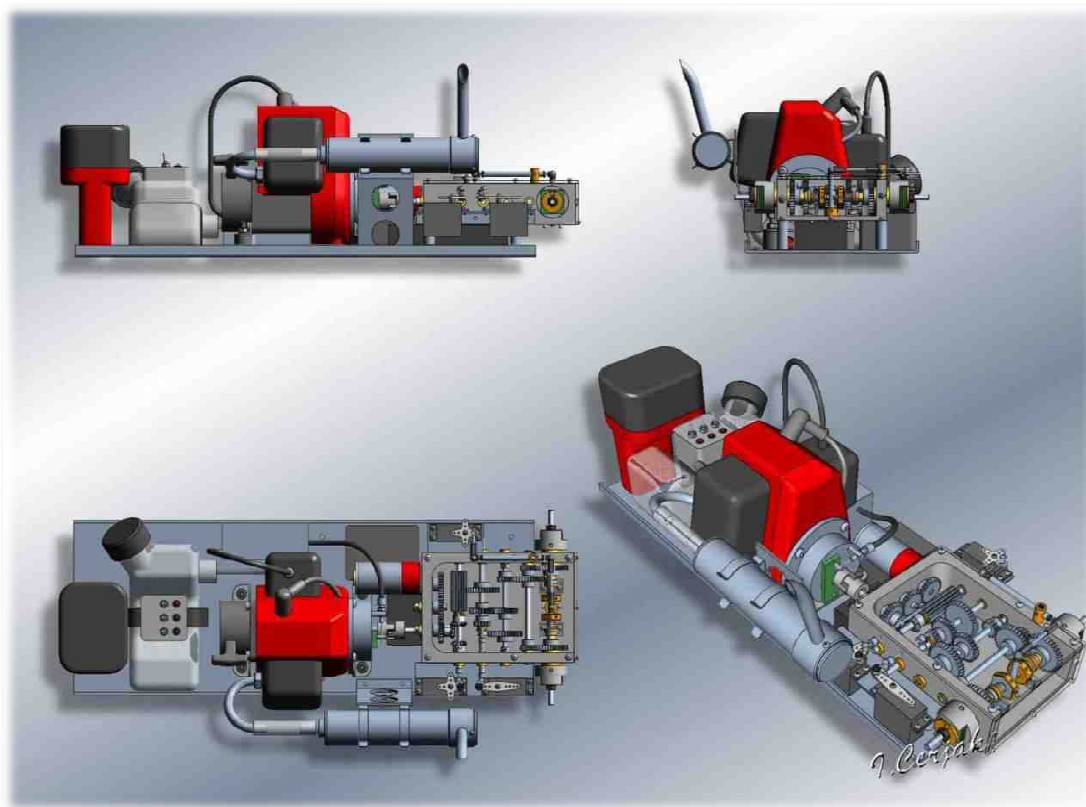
3D model zástavby motoru s převodovkou výrobce Ilja Cerjak
